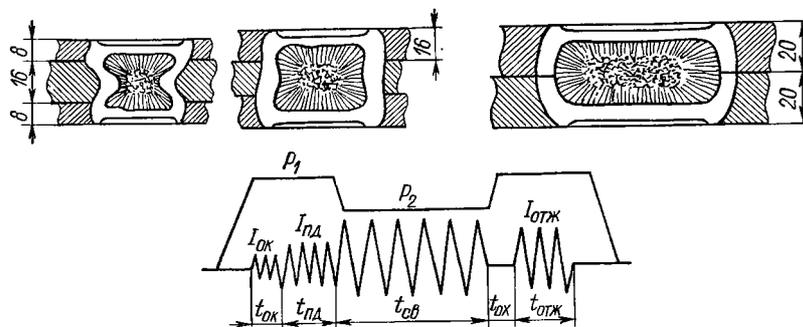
Типовая структура точечно-сварных соединений больших толщины и типовой цикл сварки для них
